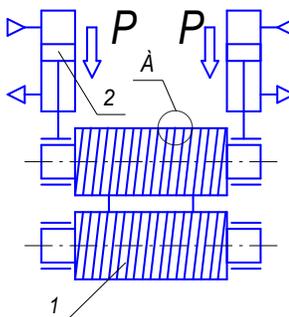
Схема стана для поверхностного упрочнения рессорных листов
